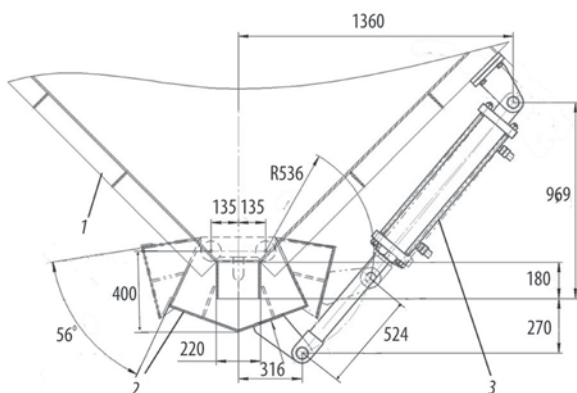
Пневматический привод бункерного затвора: 1 — корпус бункера; 2 — бункерный затвор; 3 — пневмоцилиндр
